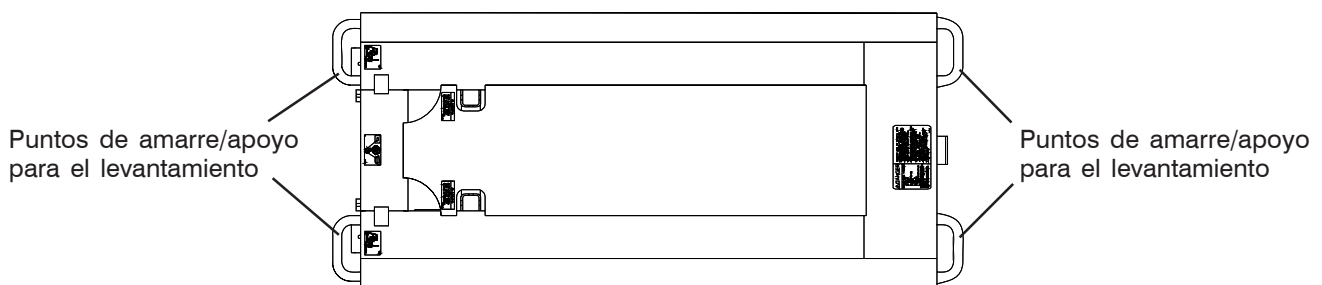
Puntos de amarre/apoyo para el levantamiento
